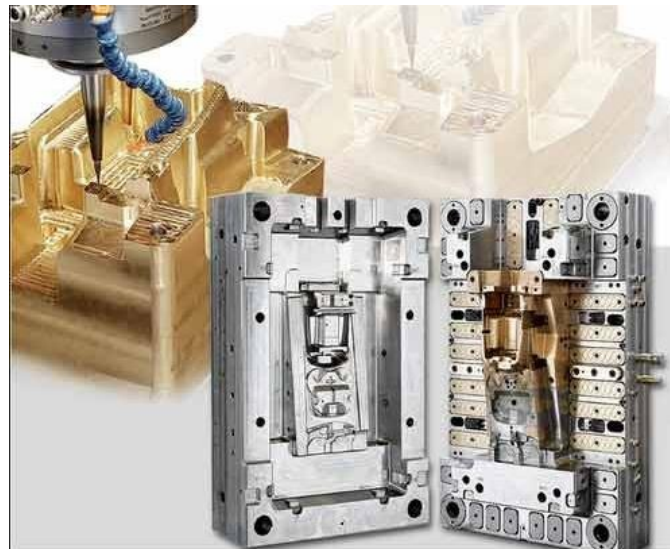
Exemplo de maquinagem e aplicação do *AMPCOLOY
